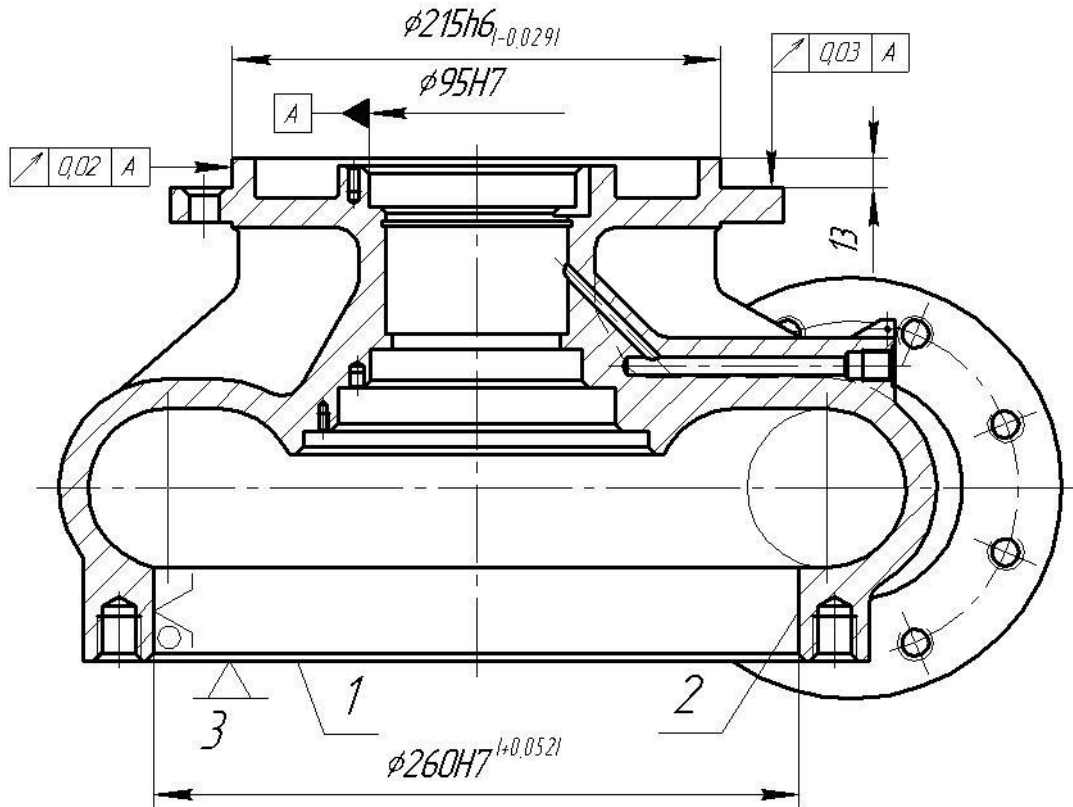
Схема базування деталі при контролі торцевого биття
